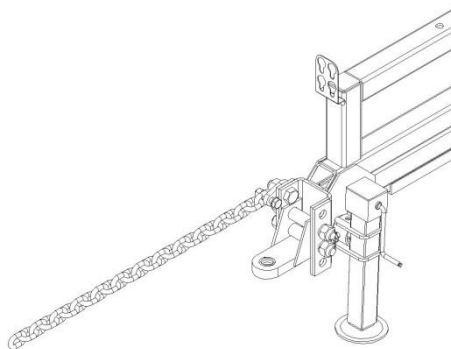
Общий вид сцепного устройства сеялки ЗС-9
